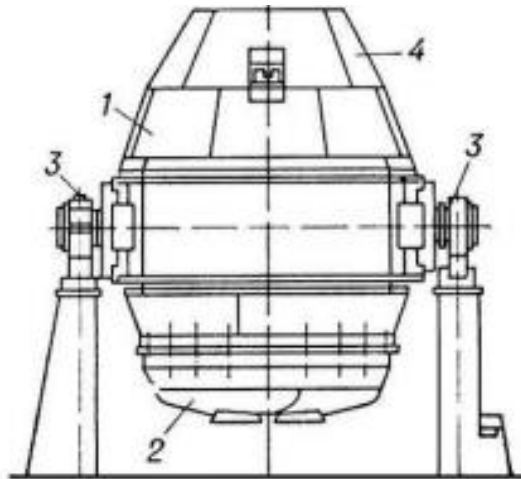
Схема кисневого конвертера: 1 – корпус; 2 – днище; 3 – опорні цапфи; 4 – горловина
